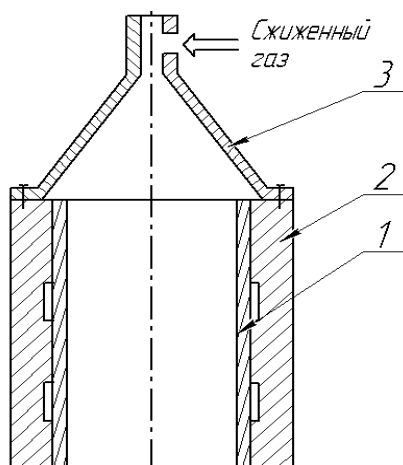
Впрыск порции сжатого газа над формообразующей полостью оснастки: 1 – заготовка кольцевая, 2 – матрица, 3 – трубка детонационная газового пресса
